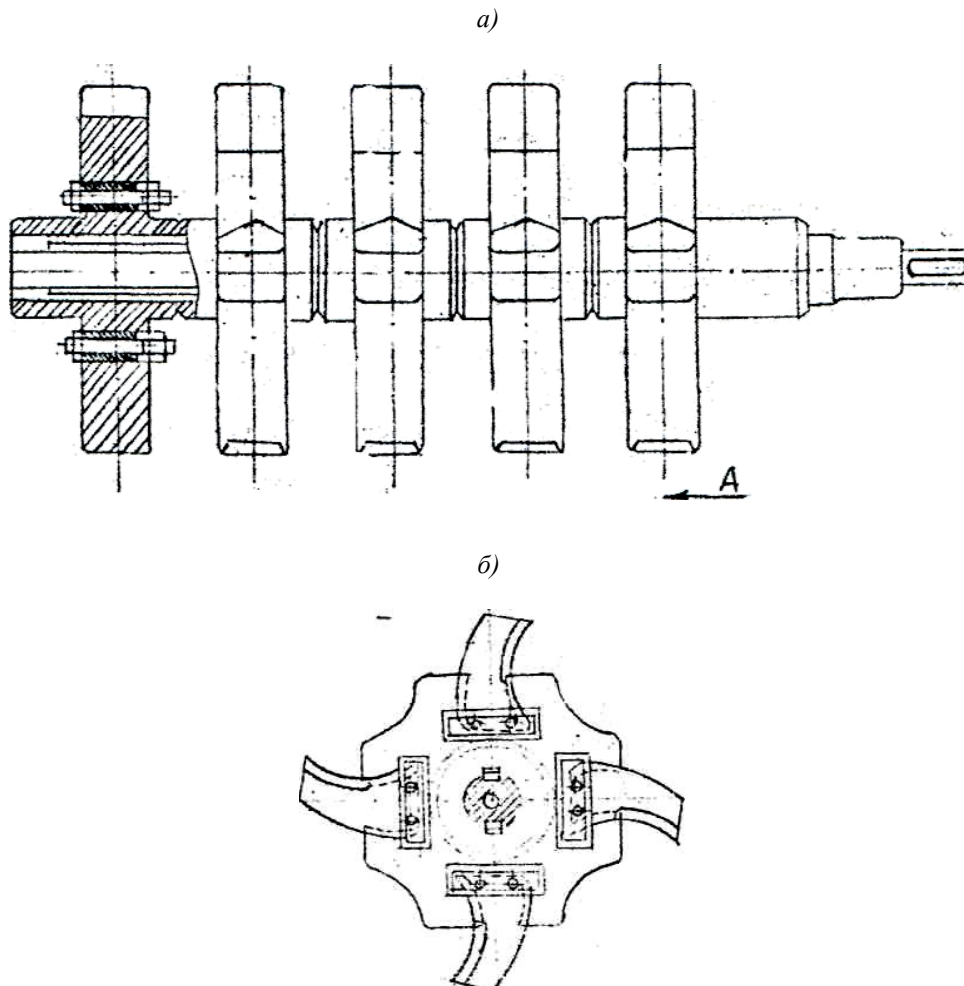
Дробящий валок: а) разрез по А-А; б) – поперечный разрез звездочки валка
